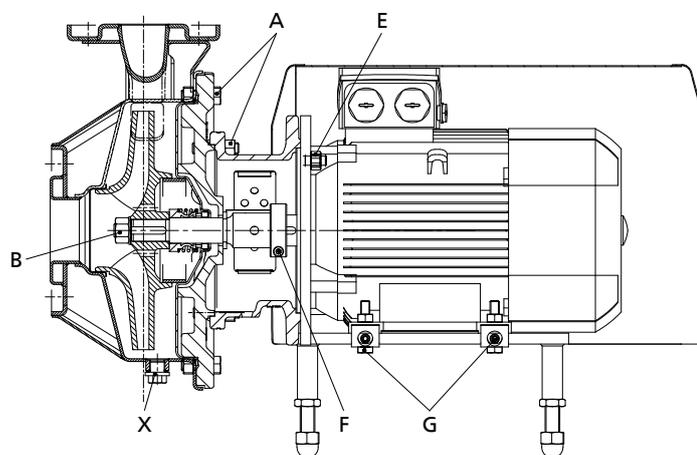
Ubicación de los tornillos para Etachrom B 050-025-250, 050-032-250, 065-040-250, 065-050-200, 065-050-250, 080-065-200, 080-065-250, 100-080-200, 100-080-250
